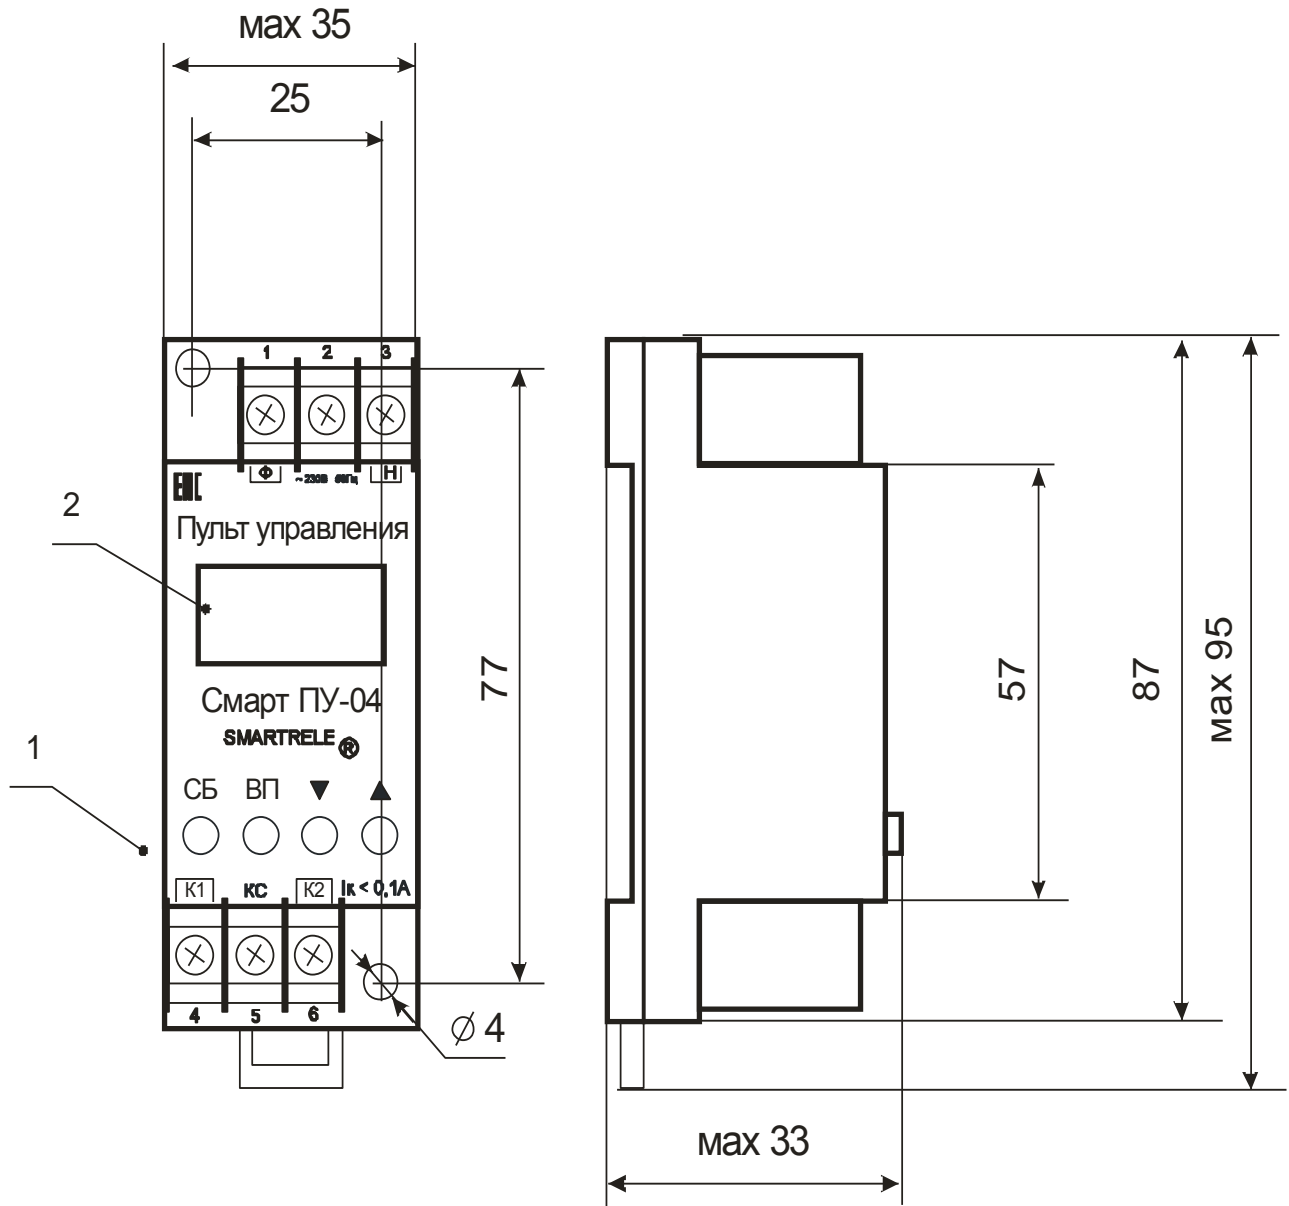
внешний вид, габаритные и установочные размеры пульта
